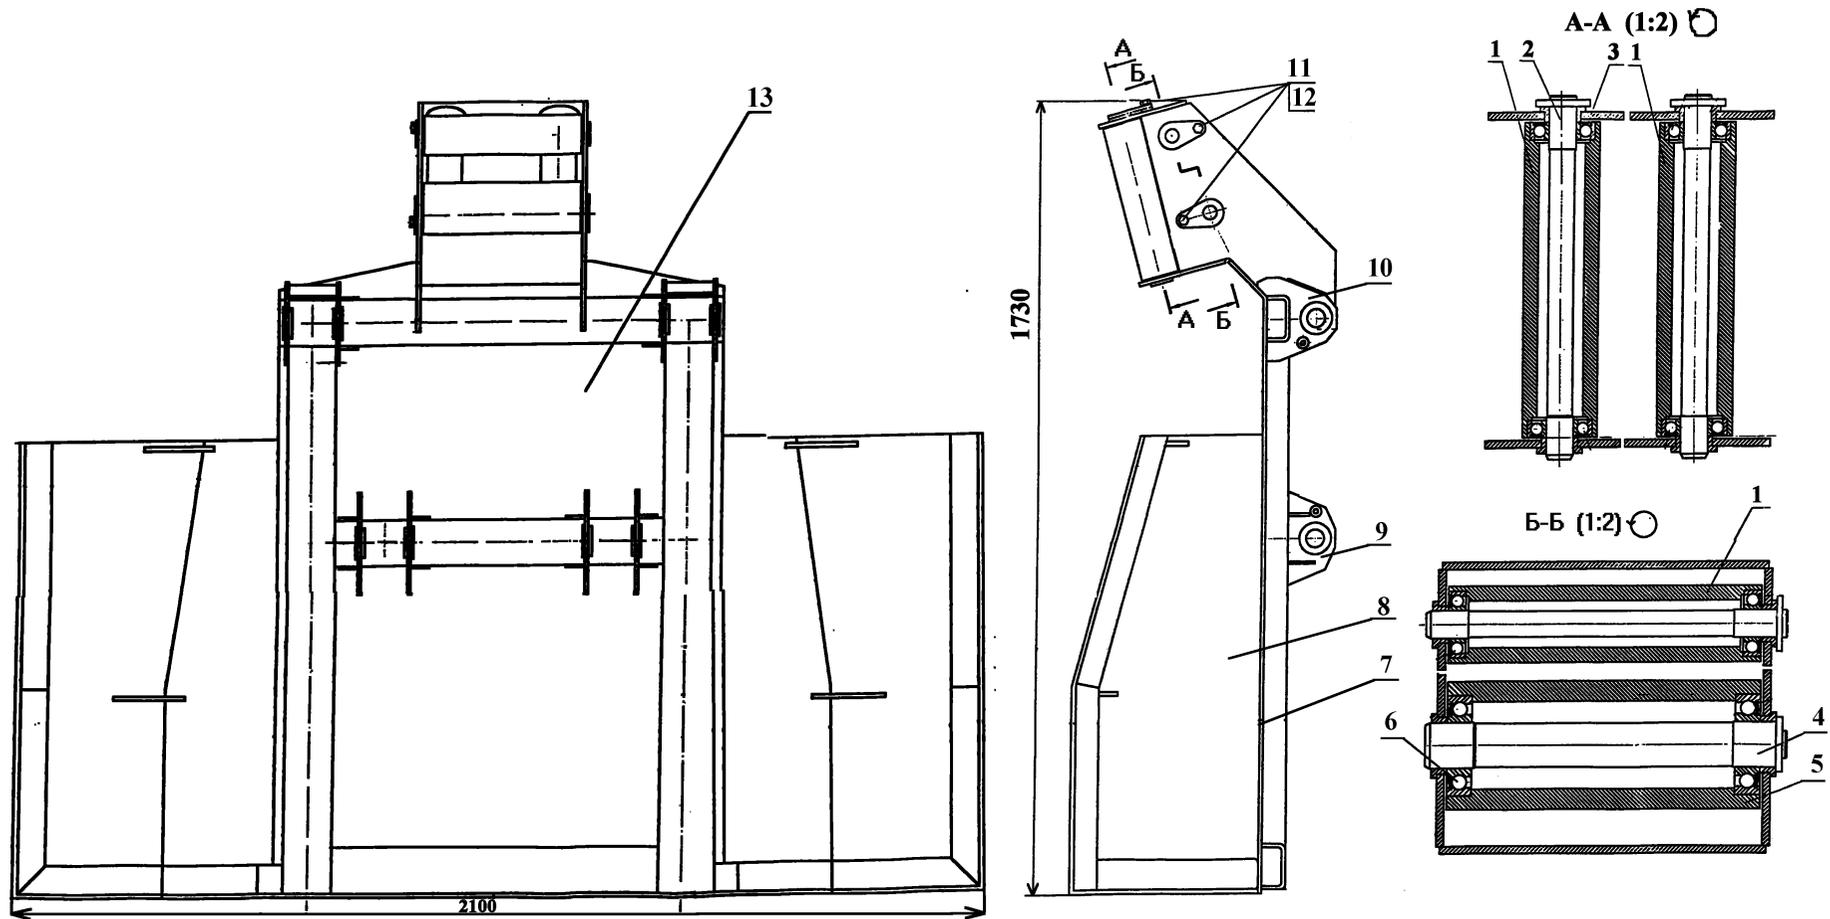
Защитно-опорный щит с аркой трелевочной машины МЛ-126: 1 – каток; 2 – ось; 3 – подшипник 60306; 4 – ось; 5 – каток; 6 – подшипник 60310; 7 – основание; 8 – боковина; 9 – балка; 10 балка; 11 – болт; 12 – гайка; 13 – щит
